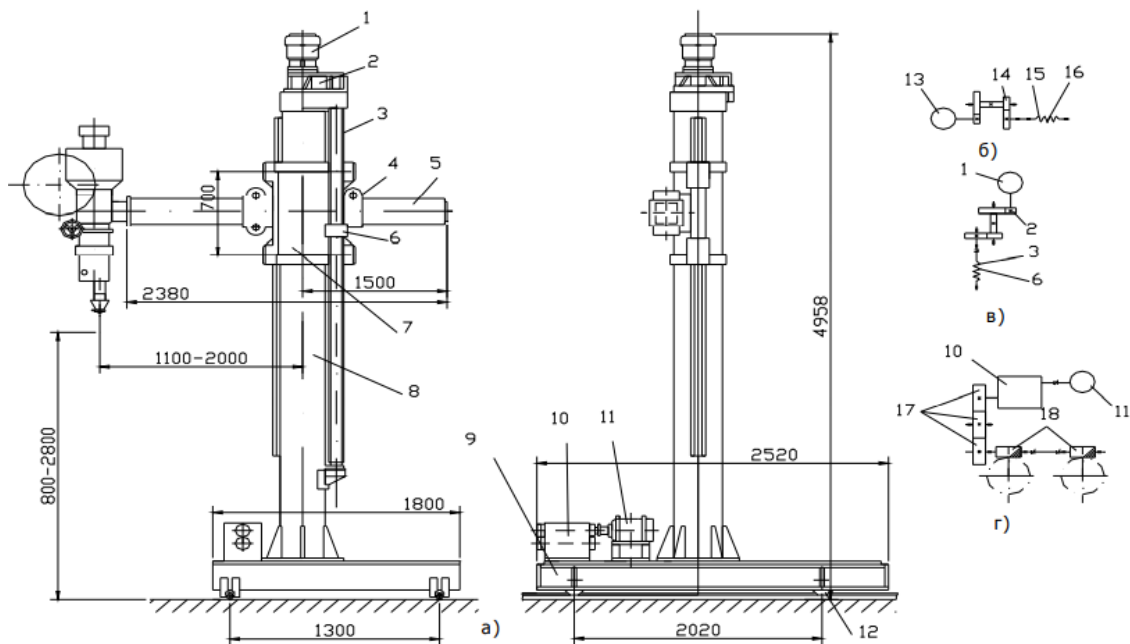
Конструкція глагольного візка типу ГТ
